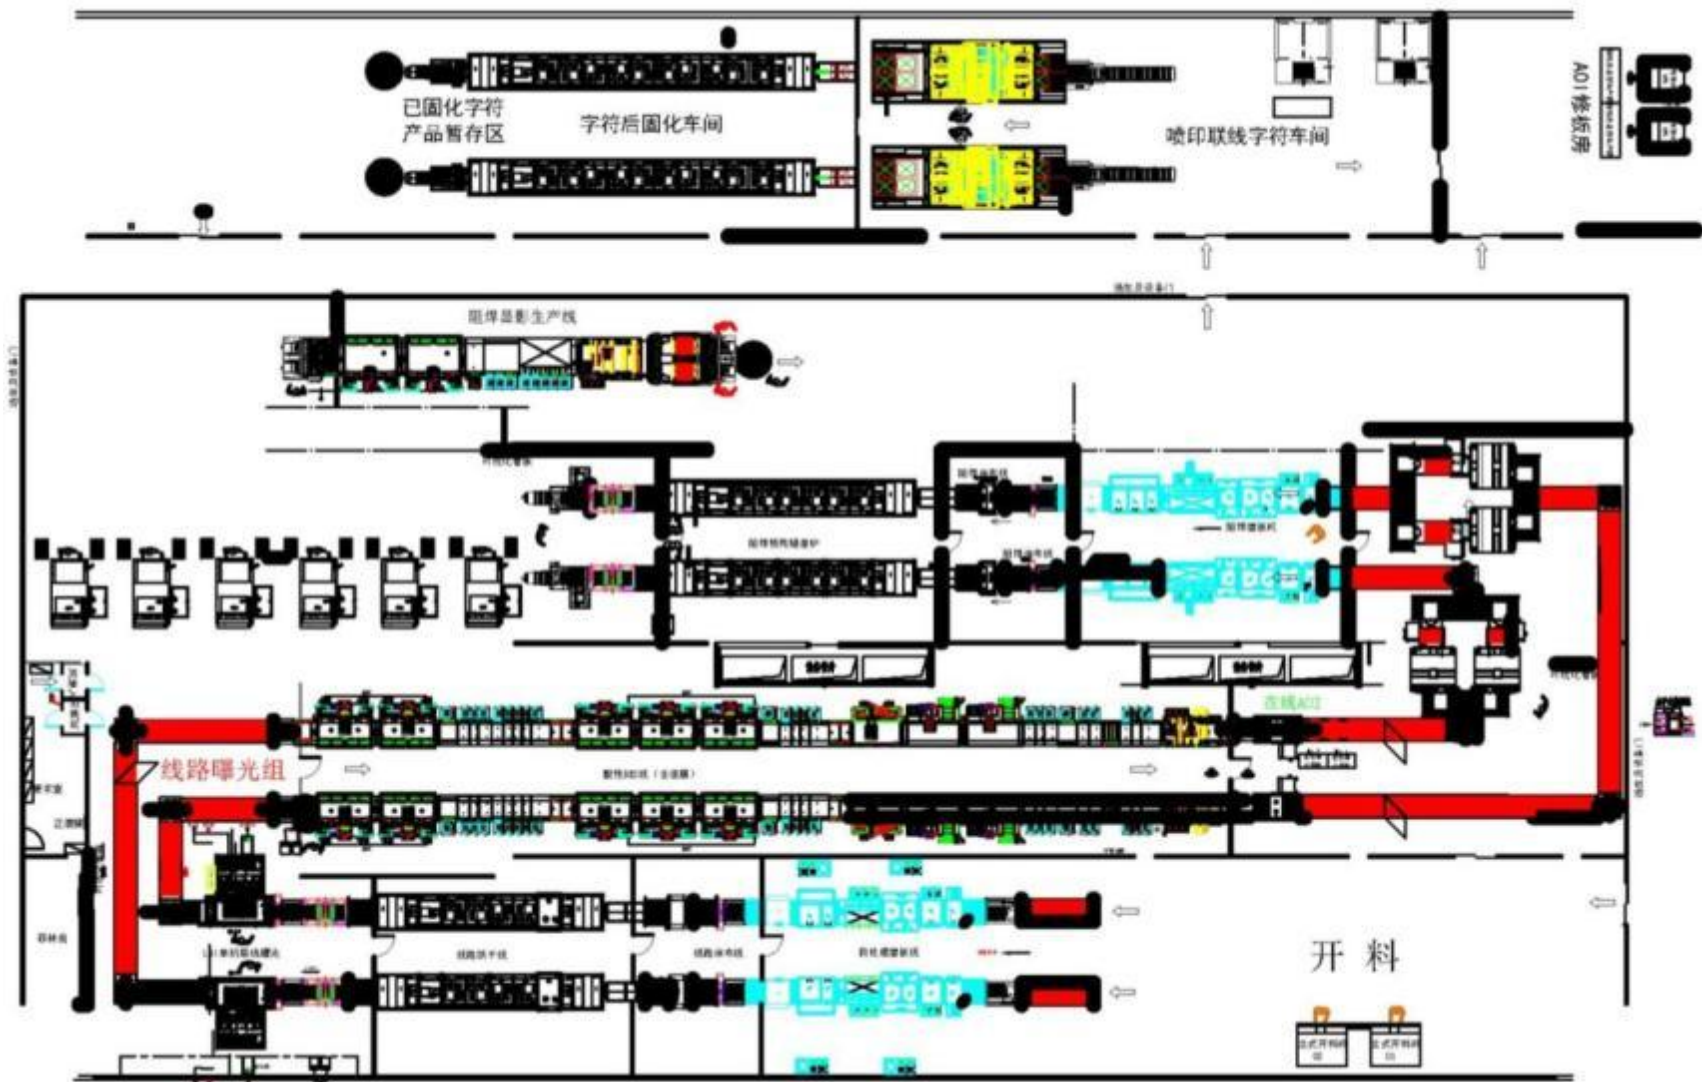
本项目二号厂房 6 楼环评阶段平面布置图
